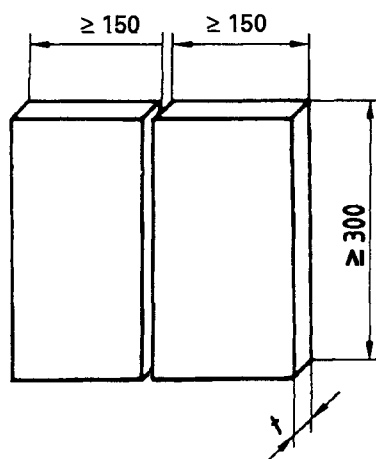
Dimensions de l'assemblage de qualification pour un assemblage bout à bout de tôles (Dimensions en mm)
